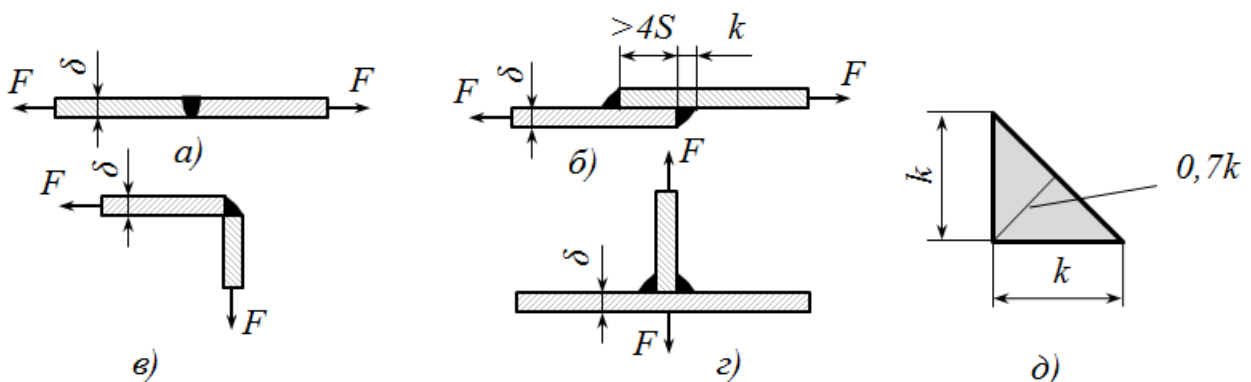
Схеми зварних з'єднань: стикове (а), внапусток (б), кутове (в), таврове (г), розрахункова схема перерізу зварного шва (д)
